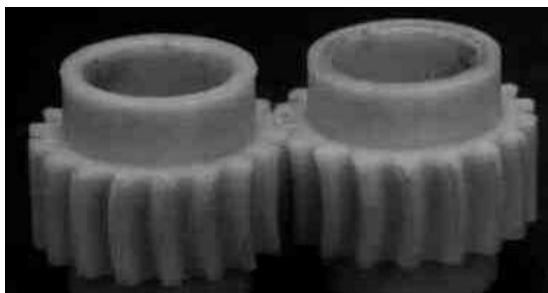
Циліндричні колеса з гвинтовими зубцями, нарізані РК-способом
